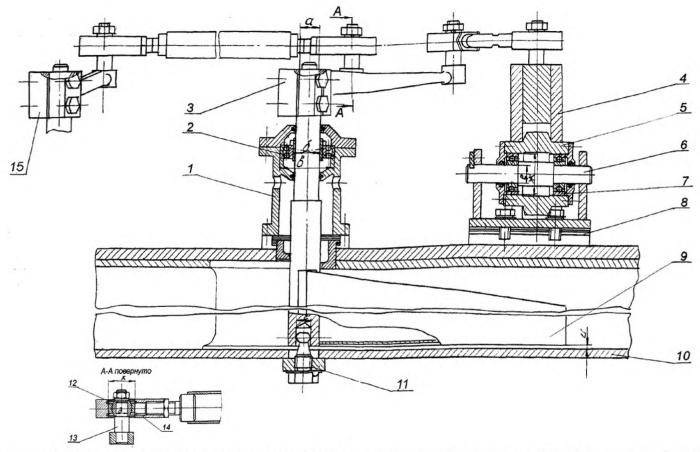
Схема центровки корпусов подшипников относительно вала
